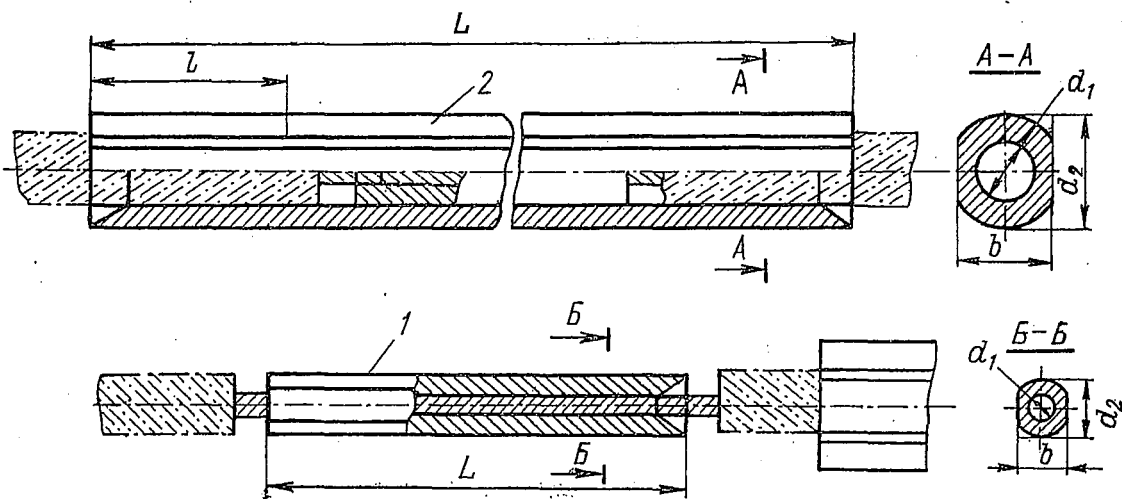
Прессуемый соединитель для сталеалюминиевых проводов
